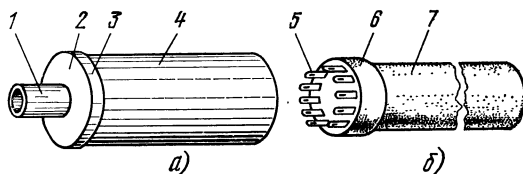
Общий вид блока термодатчиков: а) в металлическом корпусе; б) в пластмассовом корпусе:
